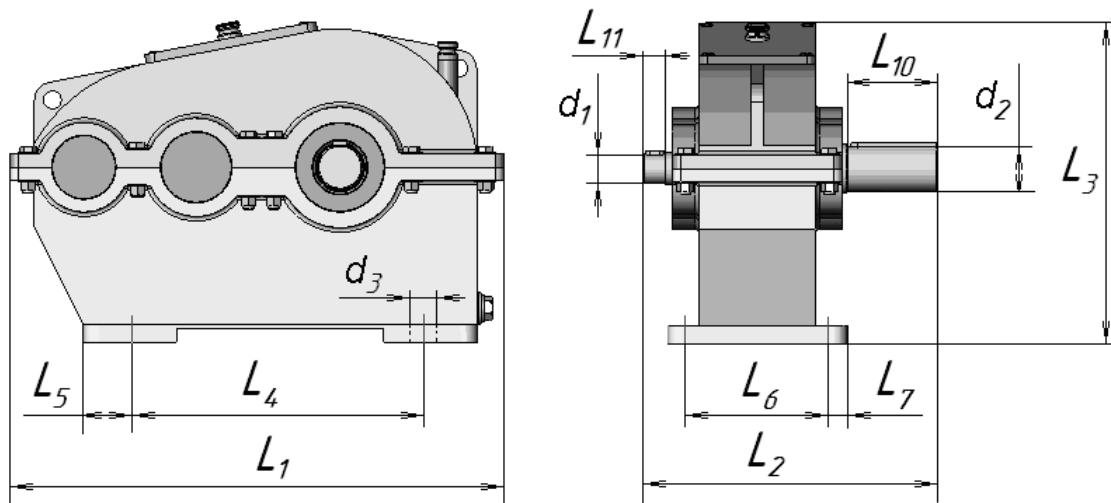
К определению присоединительных и габаритных размеров цилиндрического редуктора
